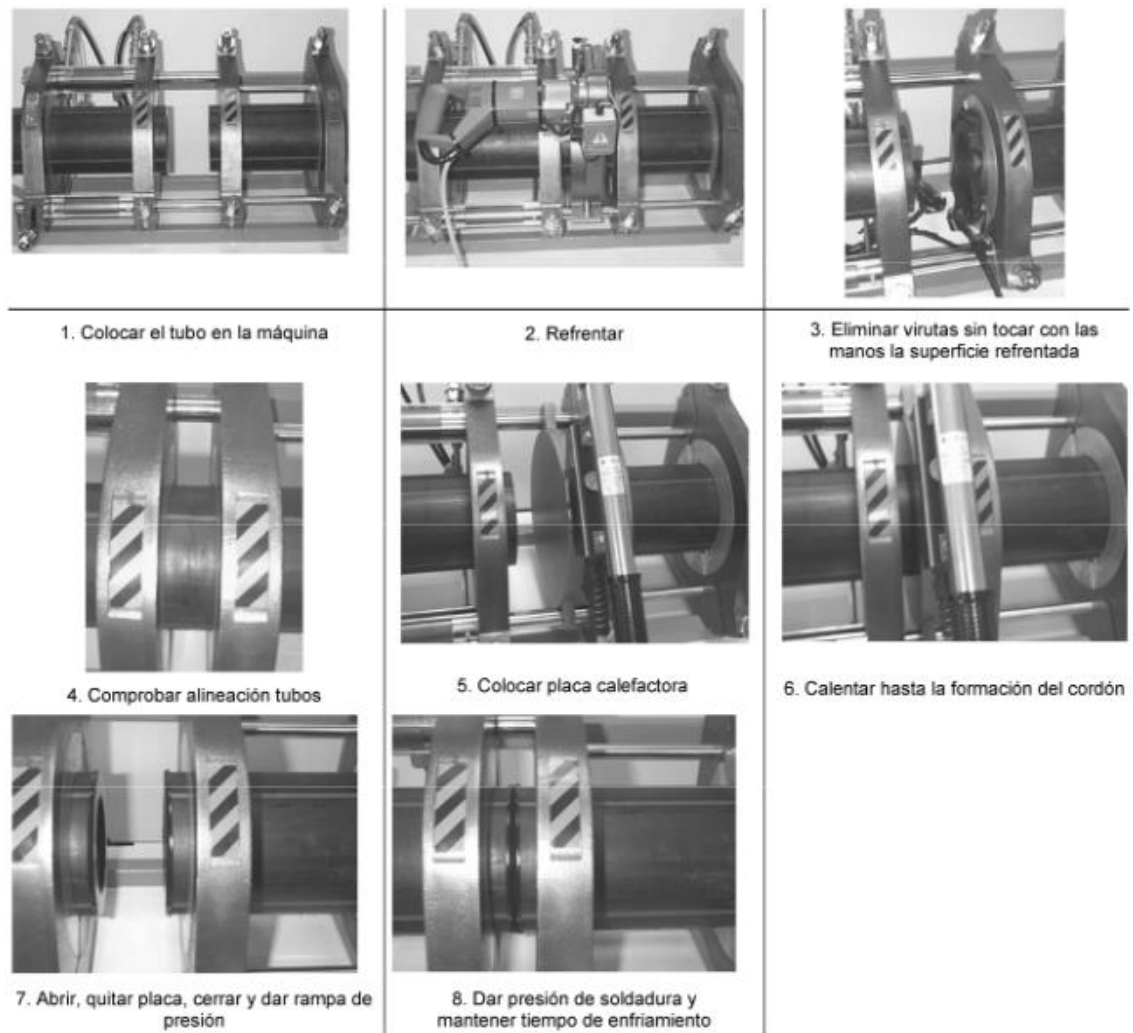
Pasos del procedimiento de unión por soldadura
